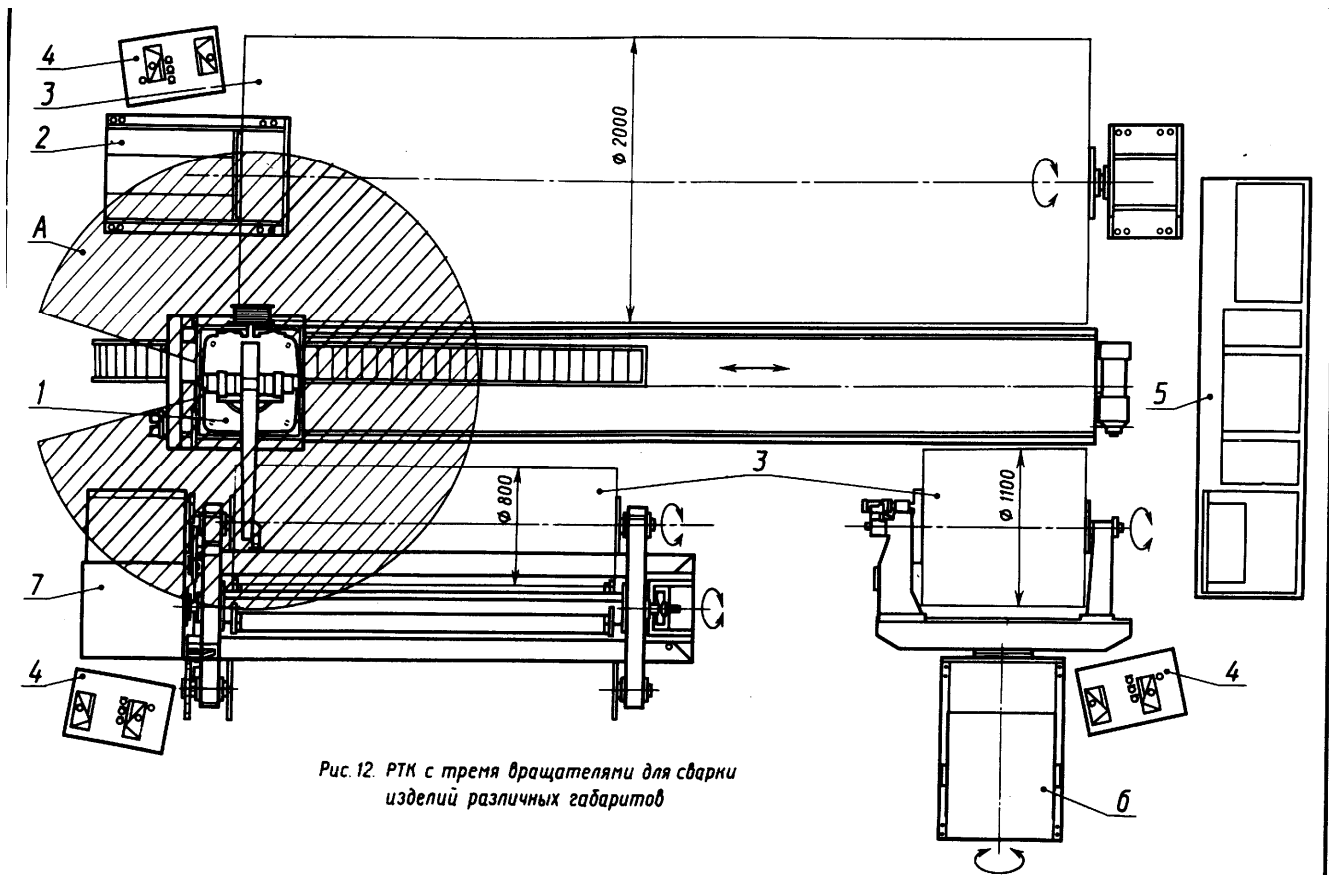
РТК с тремя вращателями для сварки изделий различных габаритов
